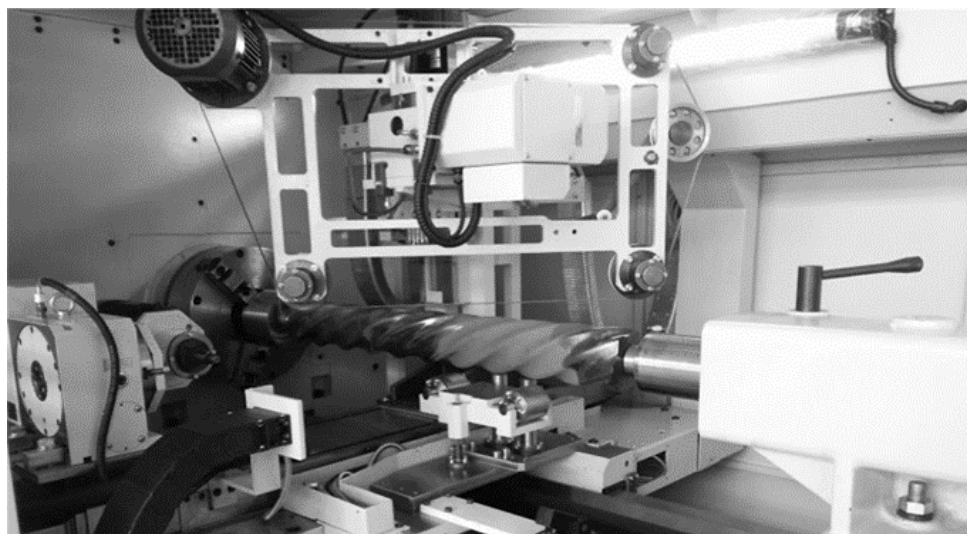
Специальный полуавтомат для ленточного шлифования роторов ВЗД
